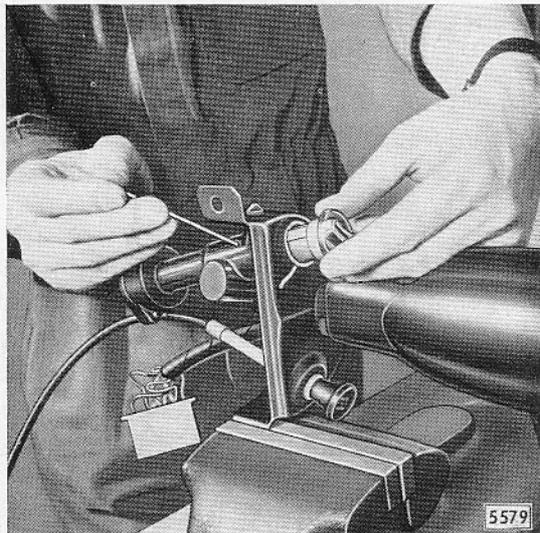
Schließzylinder aus Lenk- und Zündschloß ausbauen
